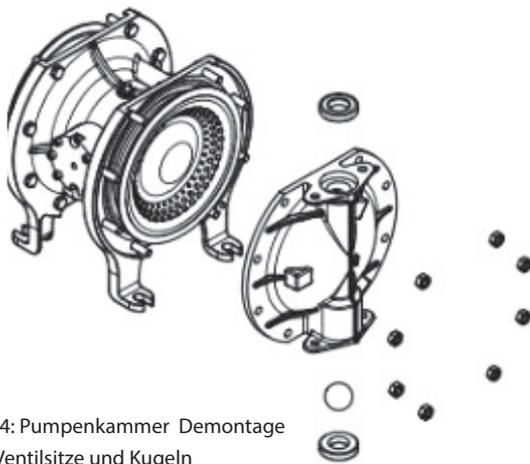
Pumpenkammer Demontage incl. Ventilsitze und Kugeln
